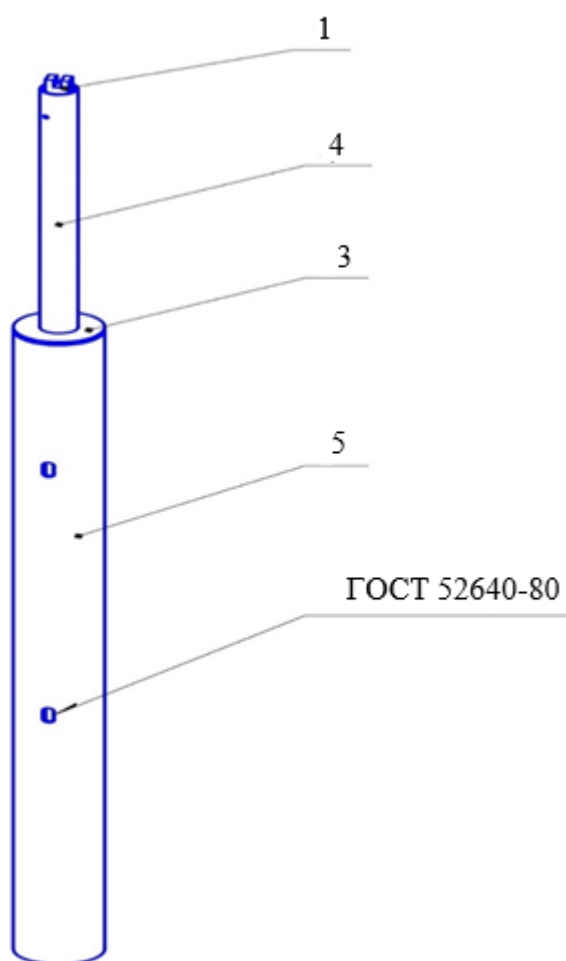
Сборка и сварка шины позиция. 2 и патрубка позиция. 5
